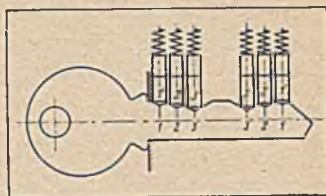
Sechskerbenschlüssel in doppelseitiger Schließung für 6-Stiftzuhaltungen
